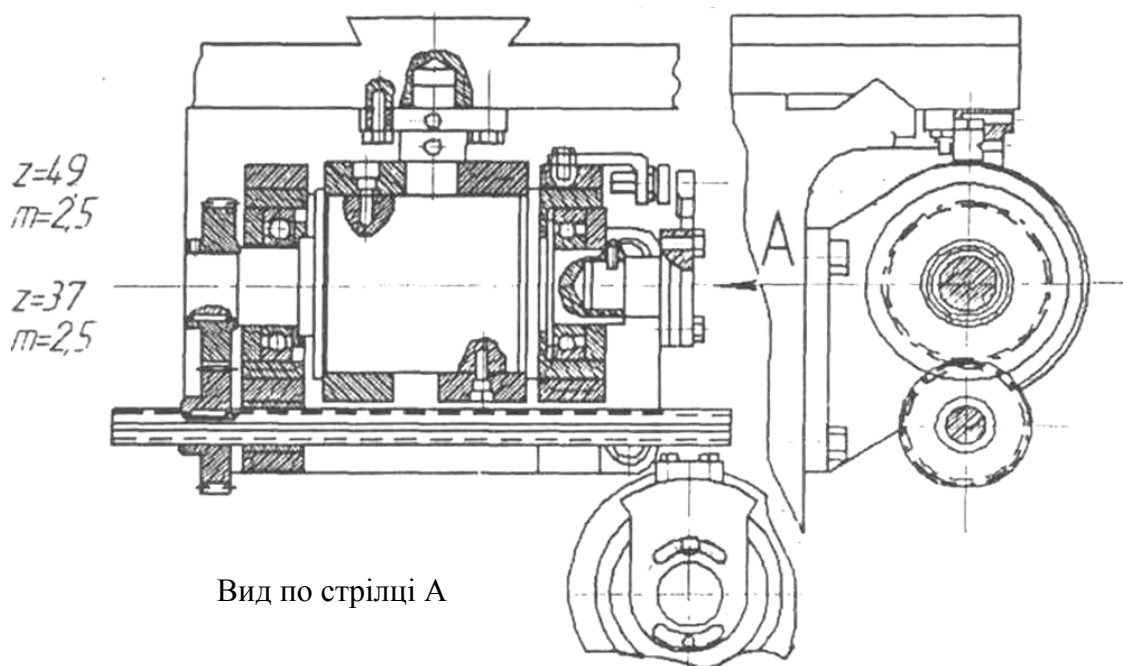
Наладка для обробки ступінчастого вала на модернізованому токарному верстаті мод. 1К62 з установленим гідрокопіювальним супортом і копіром
